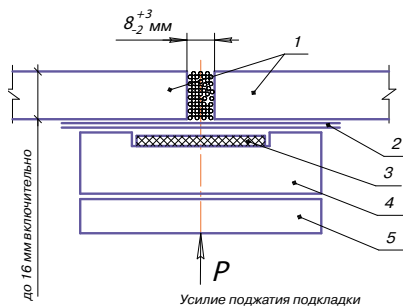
Схема сборки монтажных стыковых соединений толщиной до 16 мм включительно без разделки кромок под одностороннюю автоматическую сварку под флюсом с МХП:
